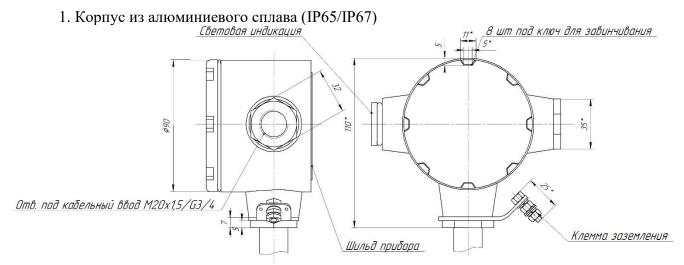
Корпус из алюминиевого сплава (IP65/IP67).
